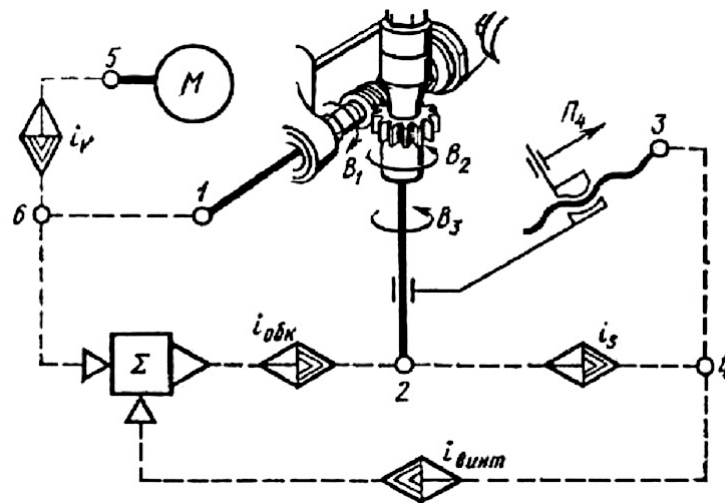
Структурная кинематическая схема станка для нарезания цилиндрических червяков и ходовых винтов чашечным резцом
